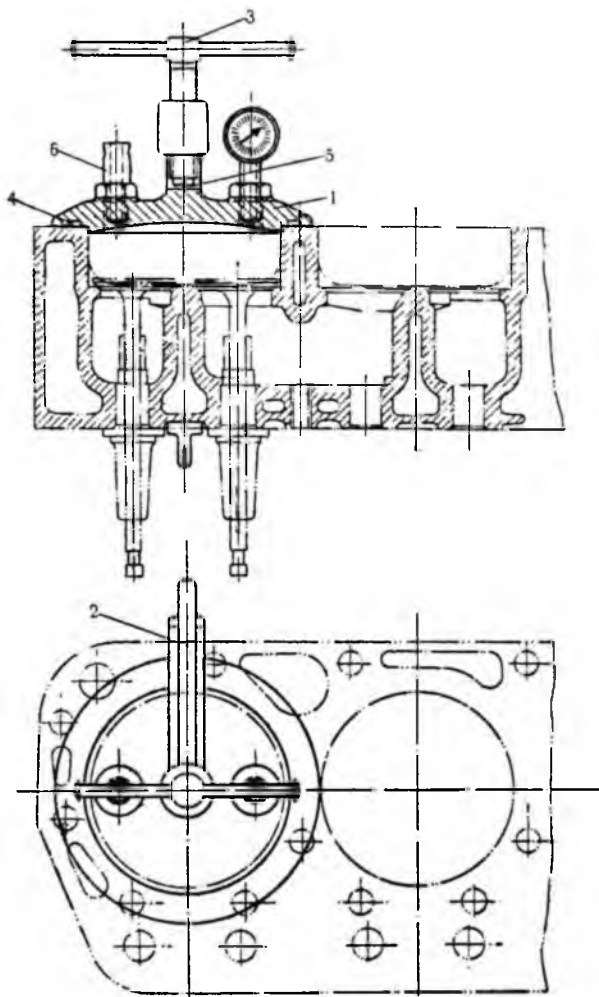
Прибор для проверки качества притирки клапанов СХТЗ:
